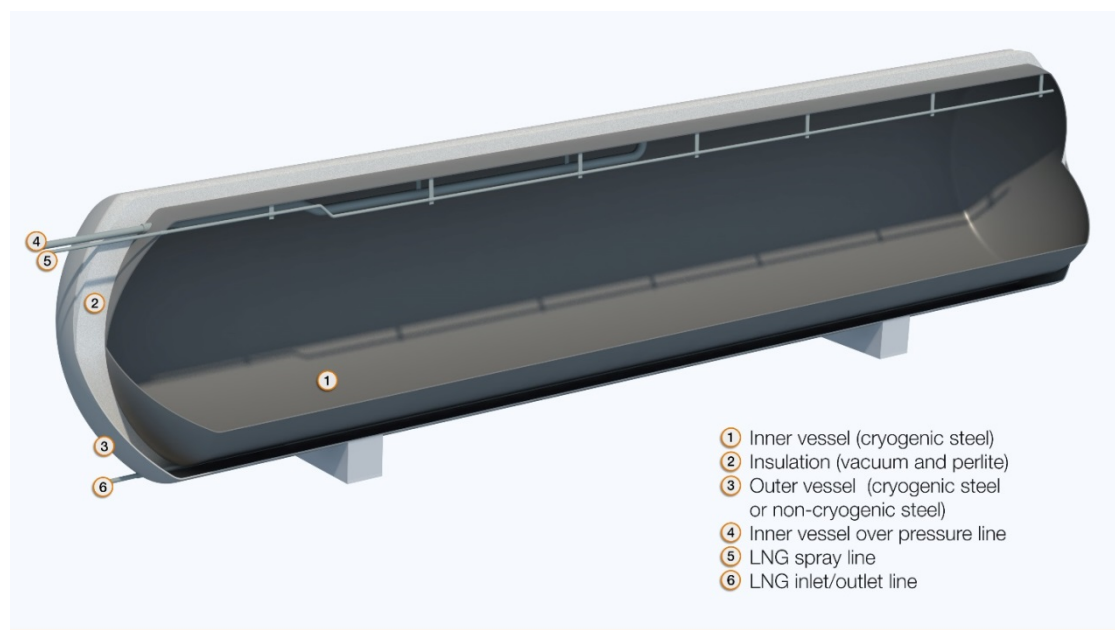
b: Serbatoio di Stoccaggio GNL – Sezione Schematica
